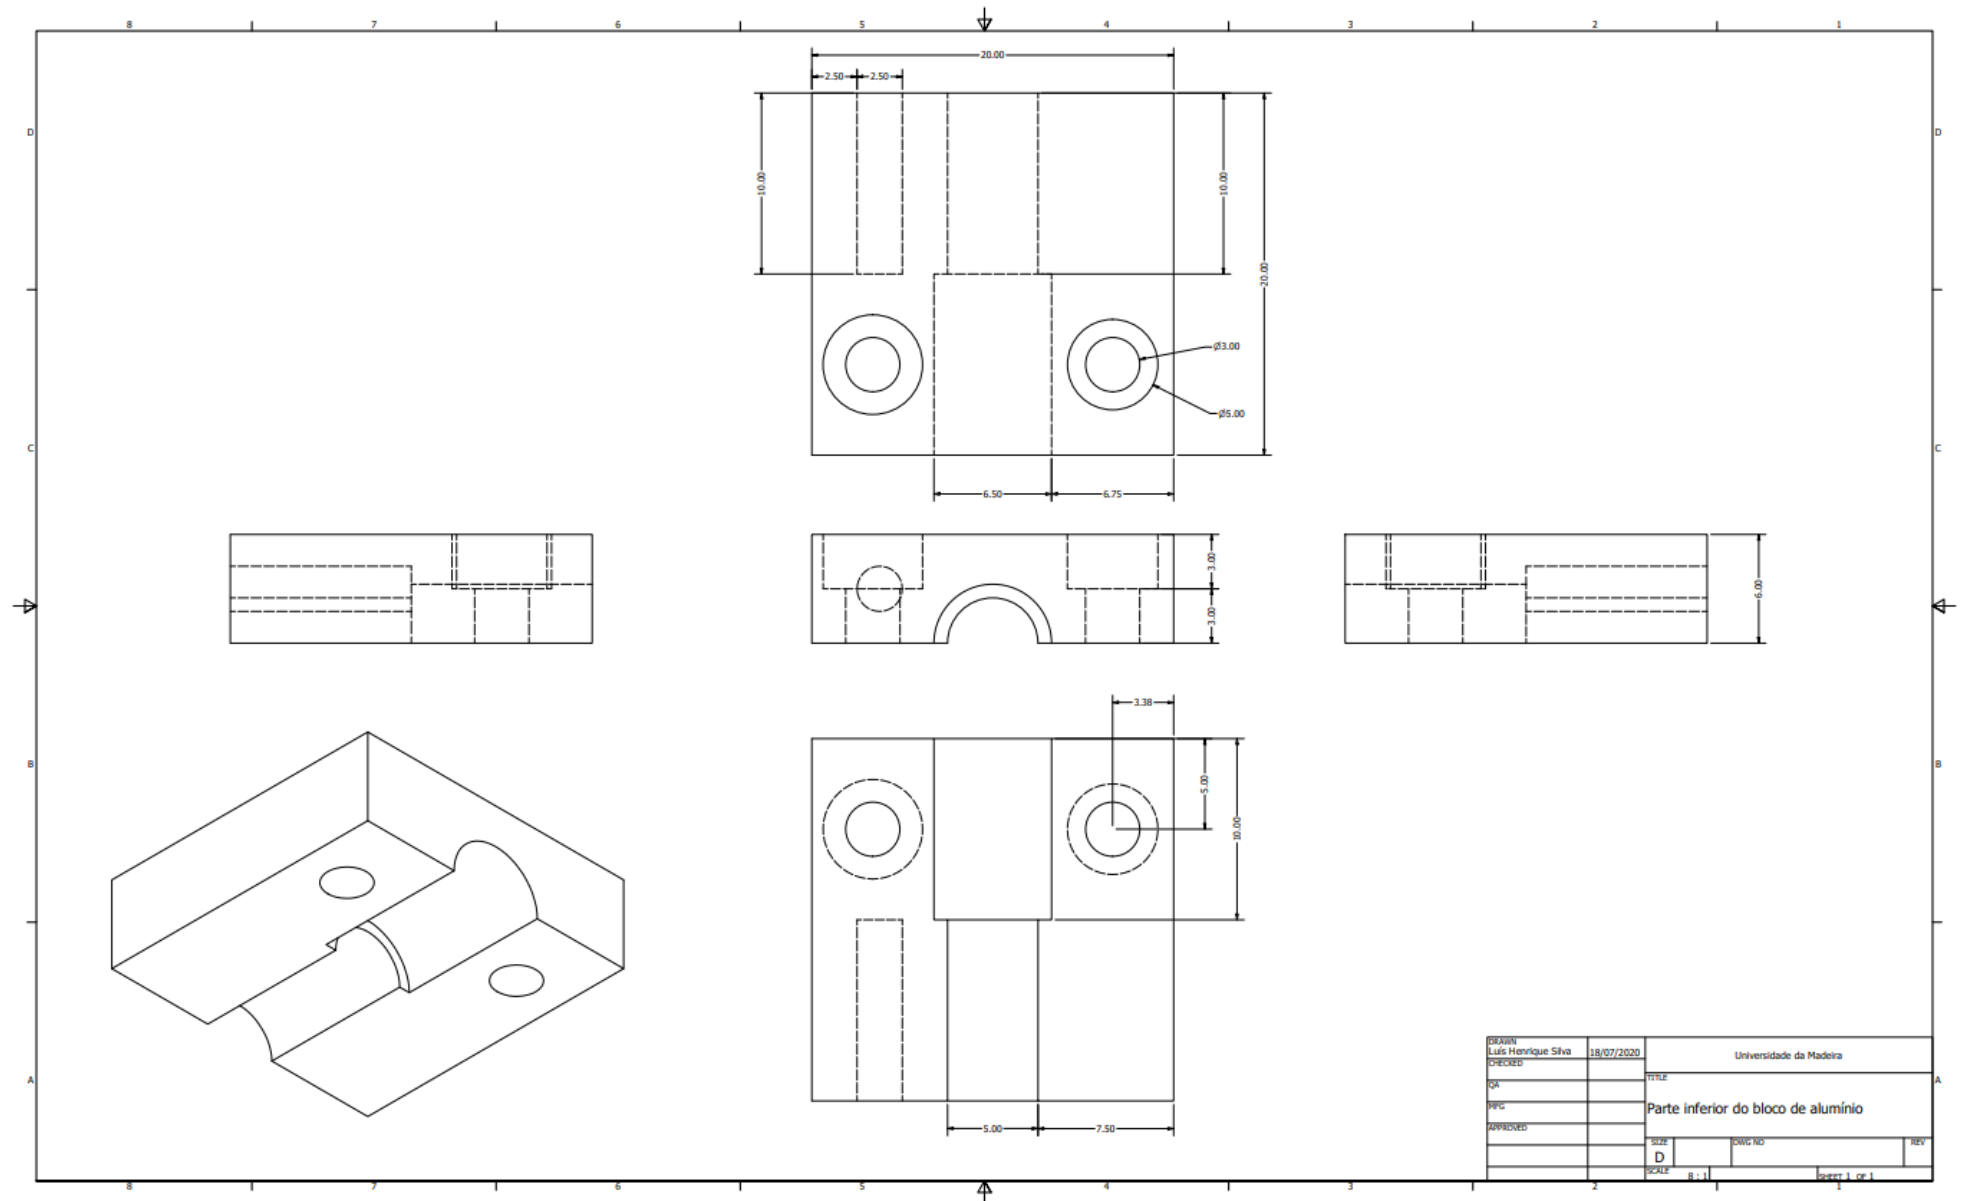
Desenho técnico da parte inferior do bloco de alumínio.
